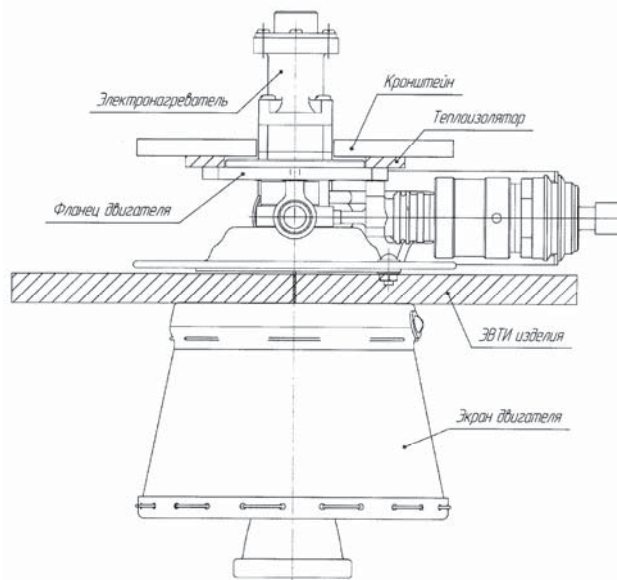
Общий вид двигателя тягой $P = 25$ Н
